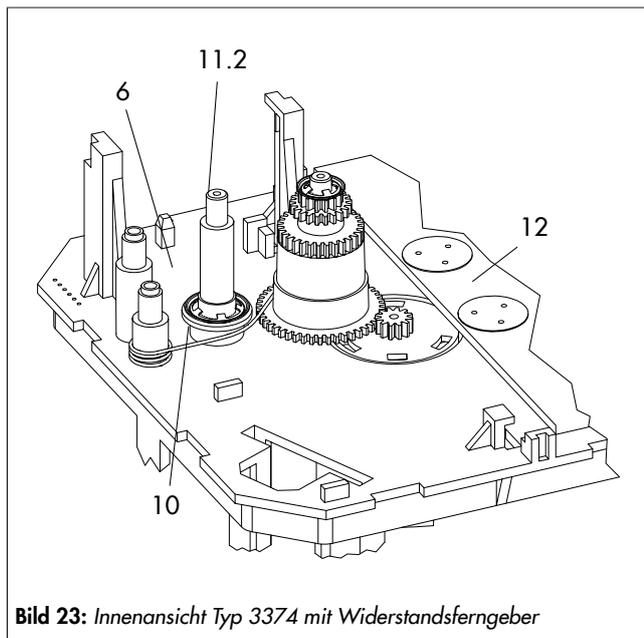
Innenansicht Typ 3374 mit Widerstandsferngeber
